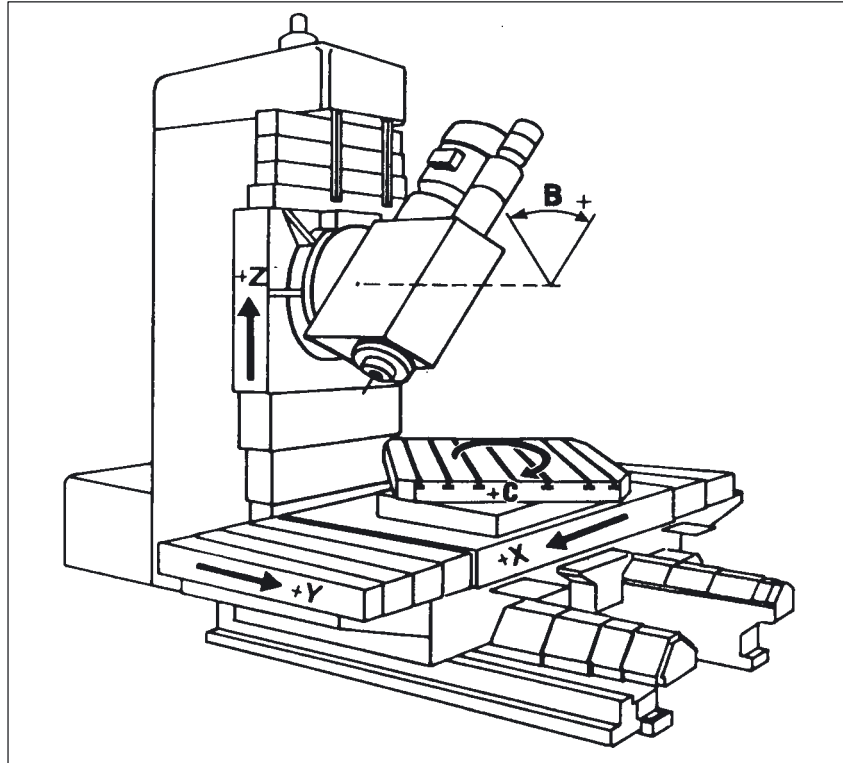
MKS mit den Maschinenachsen X, Y, Z, B, C (5Achs-Fräsmaschine)
